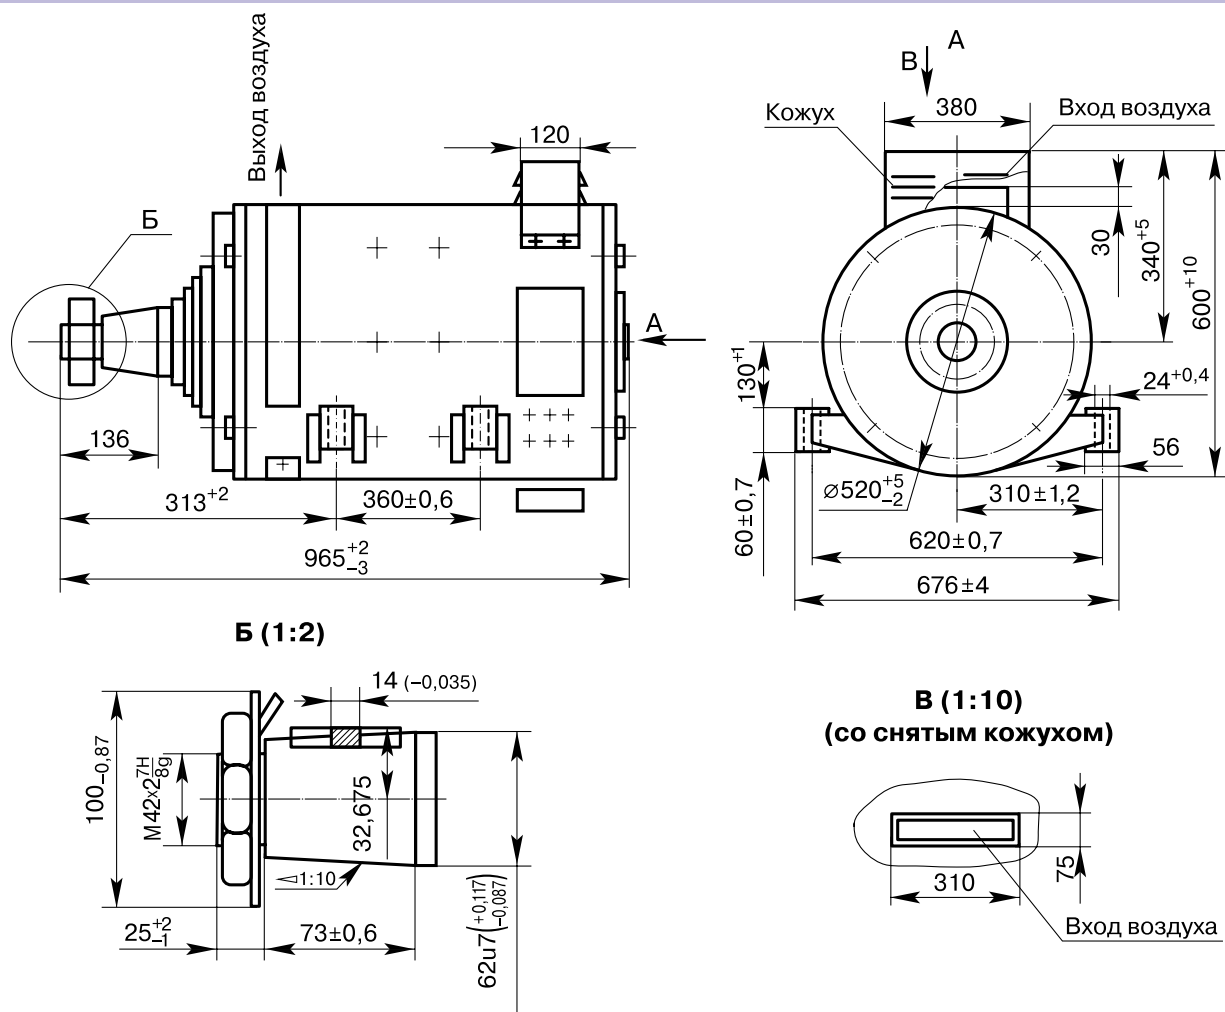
Габаритно-установочные размеры электродвигателей ДК–213МД2
